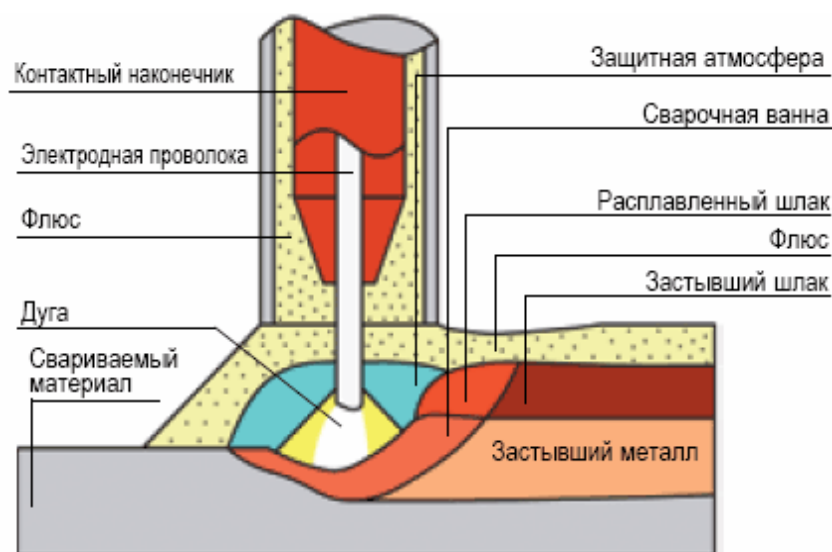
Сварка под слоем флюса[3].
